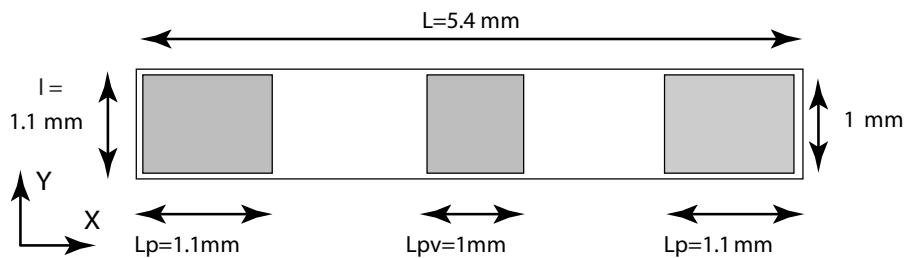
Dimensions du dispositif d'isolation de type poutre
